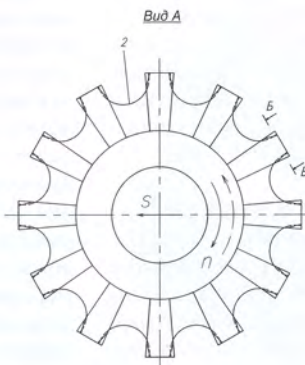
Реверсивная торцовая фреза. 1 – двухсторонний режущий зуб; 2 – стружкоотводная канавка
